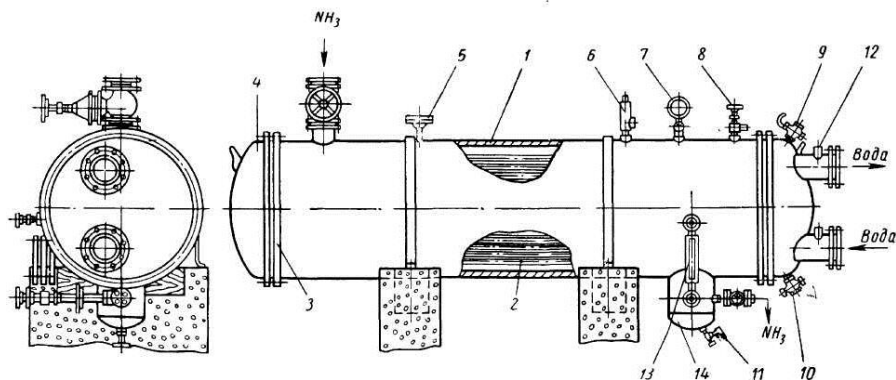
Горизонтальний аміачний кожухотрубний конденсатор: 1 – циліндричний кожух; 2 – теплообмінні труби; 3 – трубна решітка; 4 – кришка; 5 – фланець для приєднання зрівняльної лінії від ресивера; 6 – запобіжний клапан; 7 – манометр; 8 – вентиль для спуску повітря та неконденсуючих газів; 9 – вентиль для спуску повітря з водяного простору; 10 – кран для зливу води; 11 – вентиль для випуску мастила; 12 – термометрова гільза; 13 – показчик рівня; 14 – мастиловідстійник
